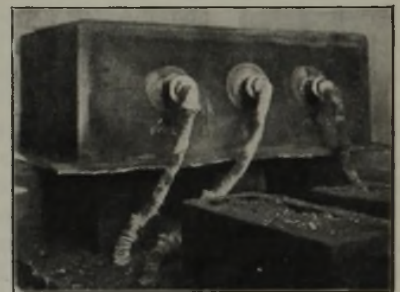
Geschweißte Blechkiste vor dem Einsatz.
